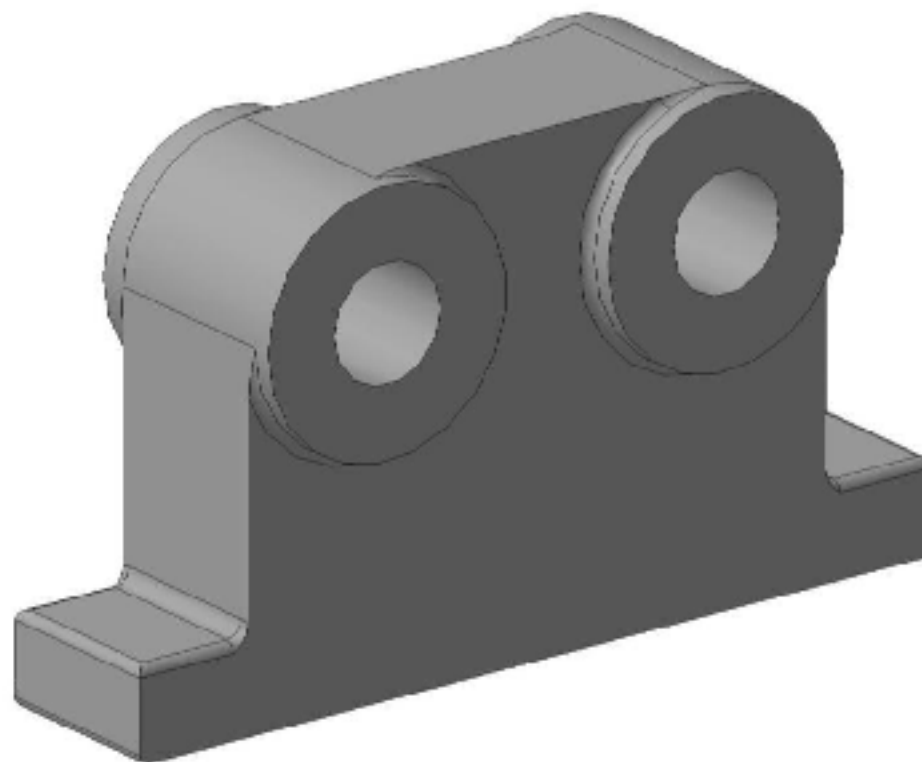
3D-модель заготовки виготовленої литтям в піщано-глинисті форми
